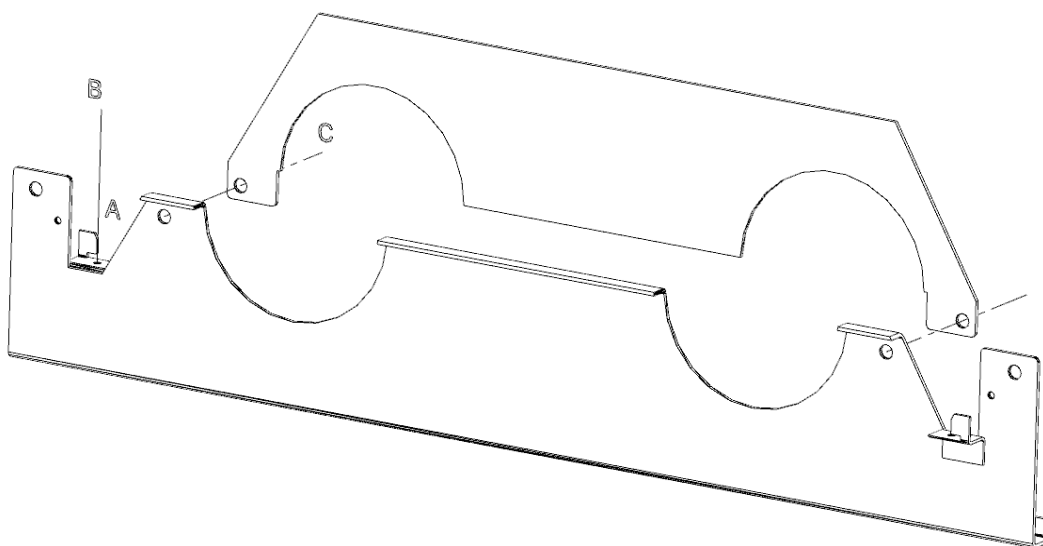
Постоянный кронштейн для крепления излучателя SBT в версии "U".
